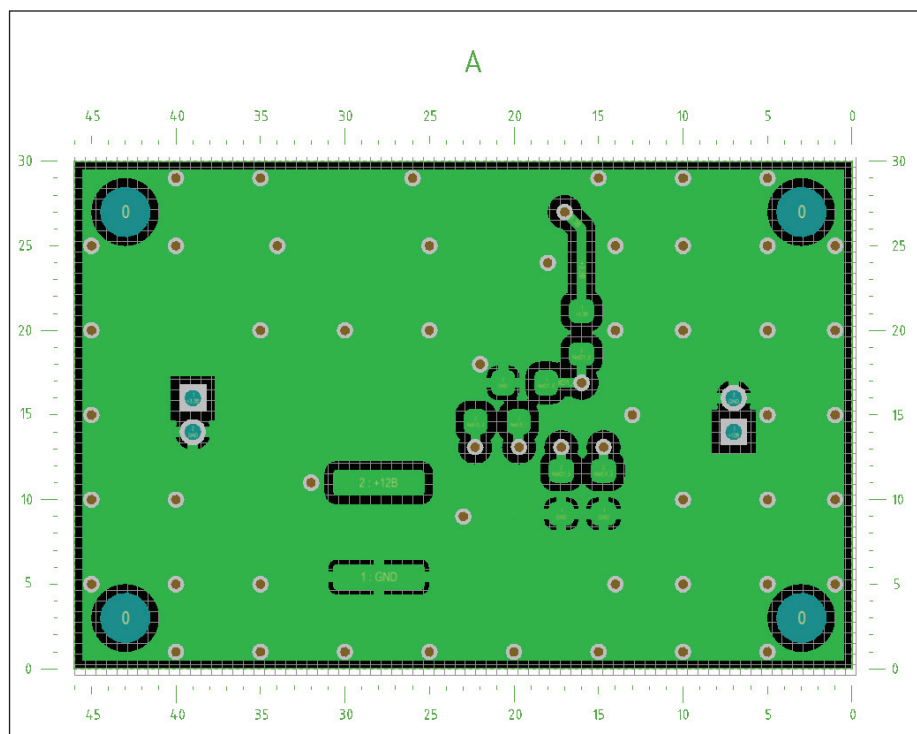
Сформированный в Altium Designer вид снизу чертежа печатной платы
